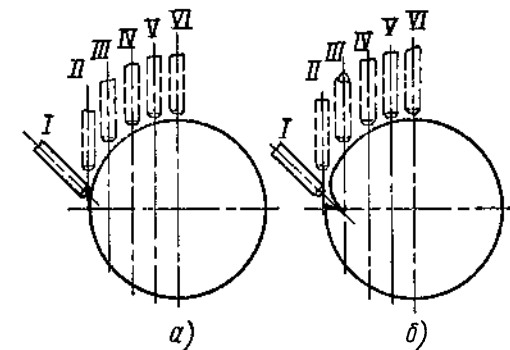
Начало резки круглой заготовки без надрубки (а) и с надрубкой (б)
